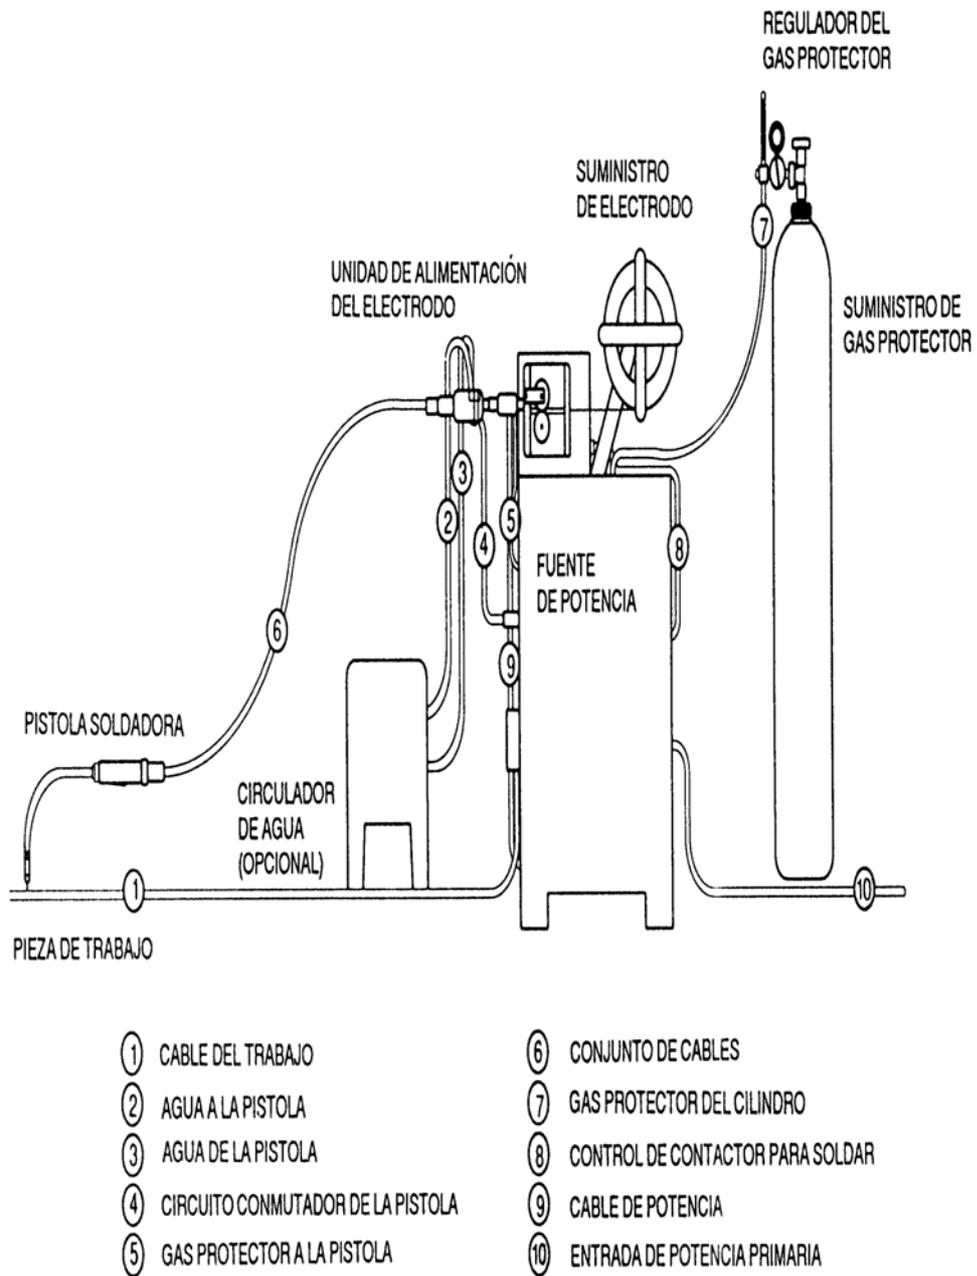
Diagrama del equipo para soldadura por arco de metal y gas
